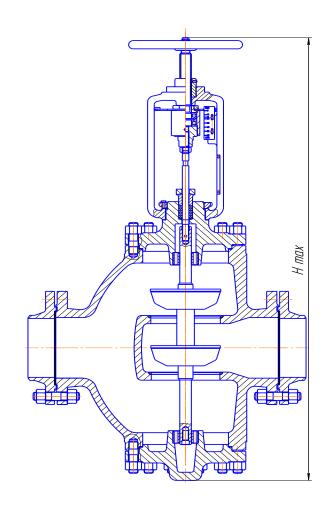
Клапан регулирующий КРД 65235 с РП
